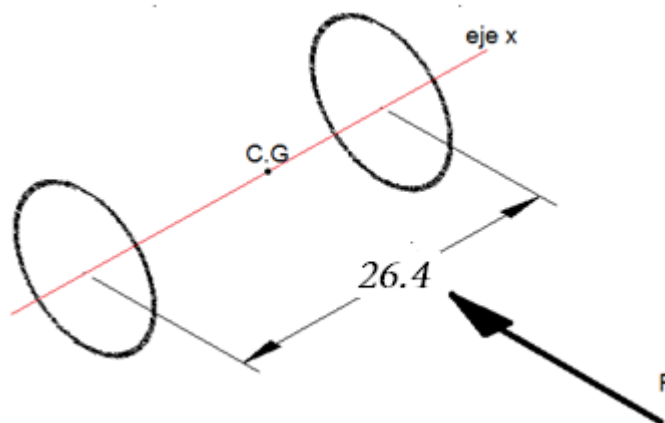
Vistas de perfil con sección transversal de soldadura y frontal con sección transversal de soldadura de muñón intermedio. Plano M-004
